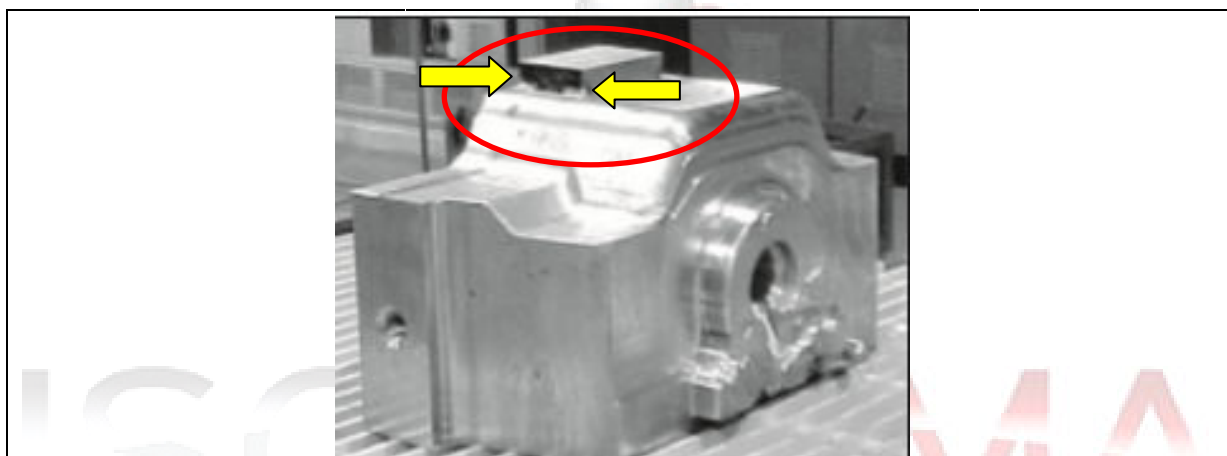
Bloco de aço com "corpo de prova" ("Coupon") fixado por solda
